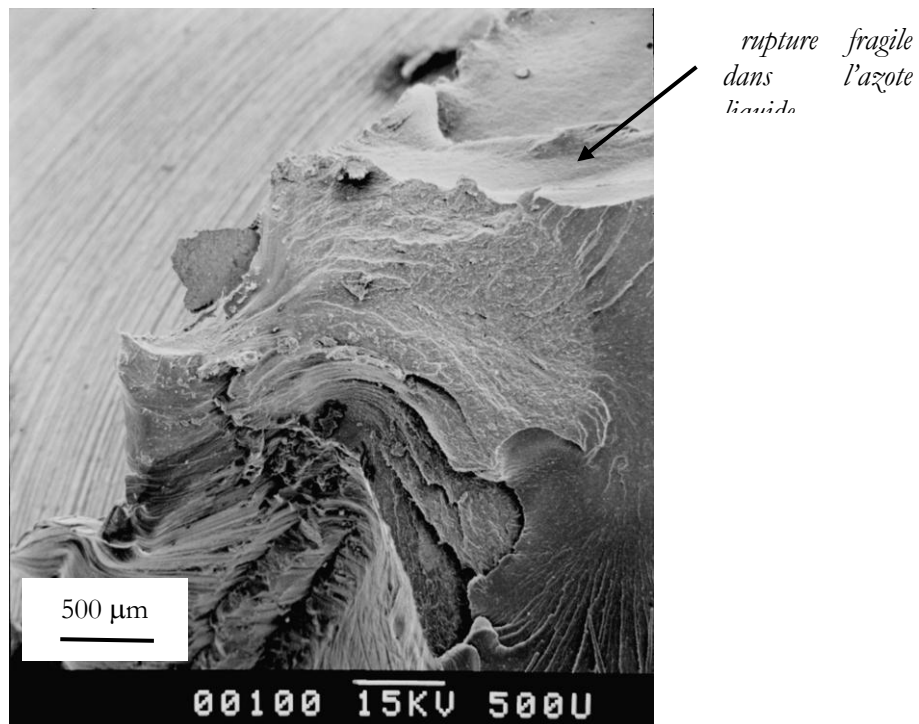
Essai AE35 – Zone d'amorçage sur joint
